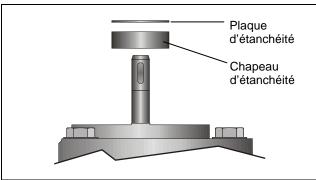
Retrait de la plaque d'étanchéité et du chapeau d'étanchéité
